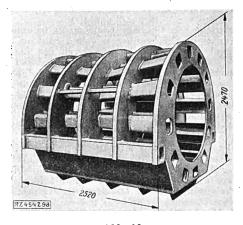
Mittels Schweißung hergestelltes Dynamogehäuse
